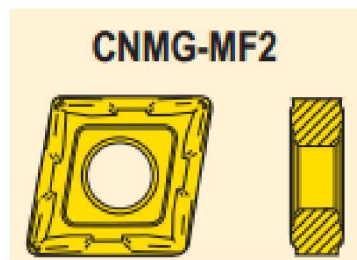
Ромбічна пластина для чорнової обробки CNMG120408 -MF5
